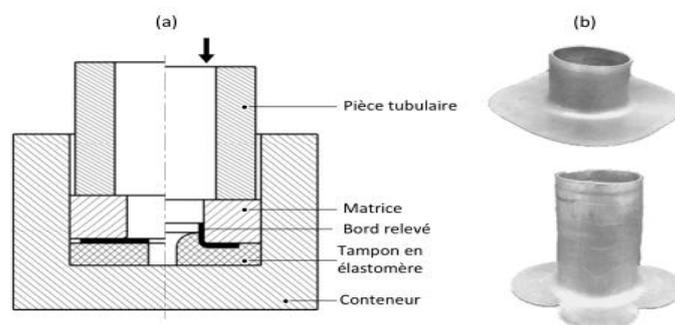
Relevage de bord par la technique de Maslennikov : (a) schéma de principe ,(b) exemples du bord relevé
